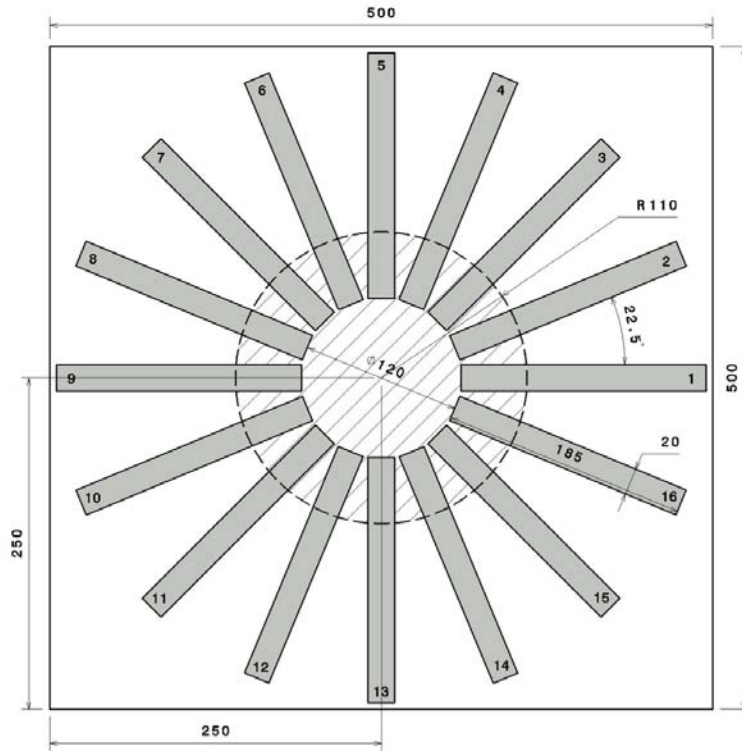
Découpe des éprouvettes DCB / ENF pour définition de la loi angulaire
